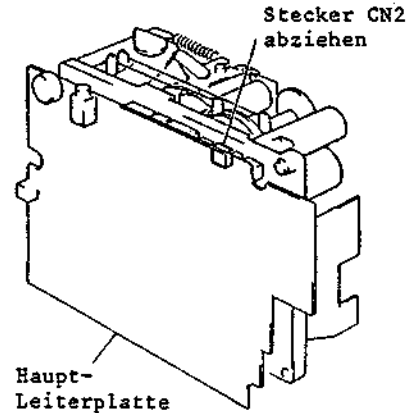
Ausbau des Vorratsteller-Rotationssensors und des Aufwickelteller-Rotationssensors
